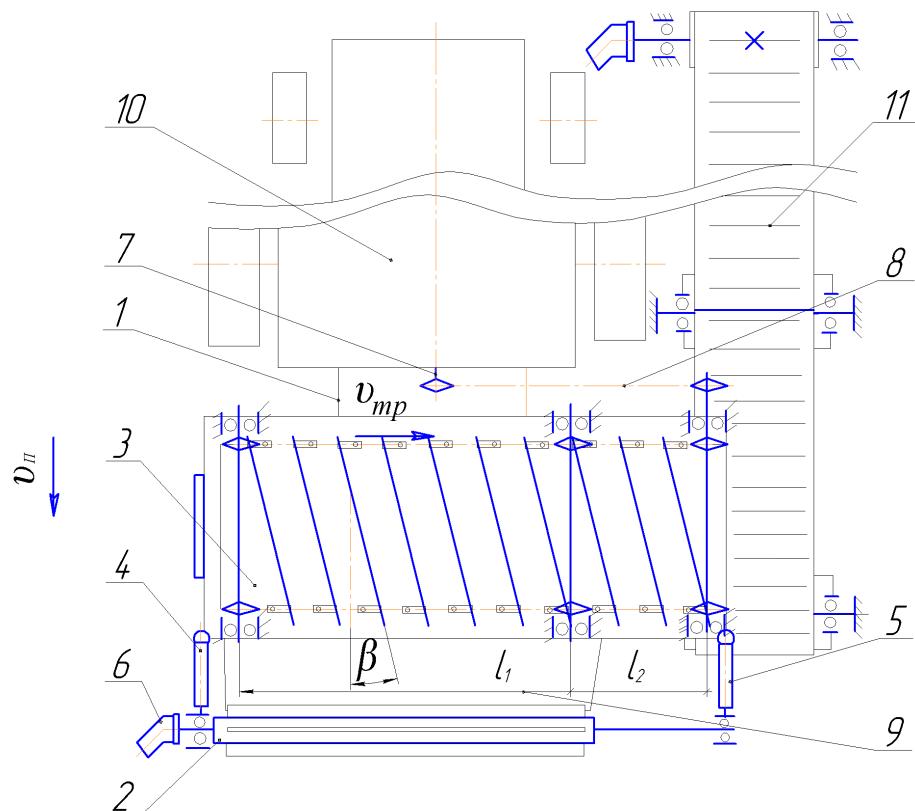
Схема роторно-цепного питателя: 1 – рама; 2 – подающий барабан; 3 – цепной транспортер; 4, 5 – гидроцилиндры; 6 – гидромотор; 7 – карданская передача; 8 – цепная передача; 9 – скатная доска; 10 – базовый трактор; 11 – отгрузочный транспортер.
